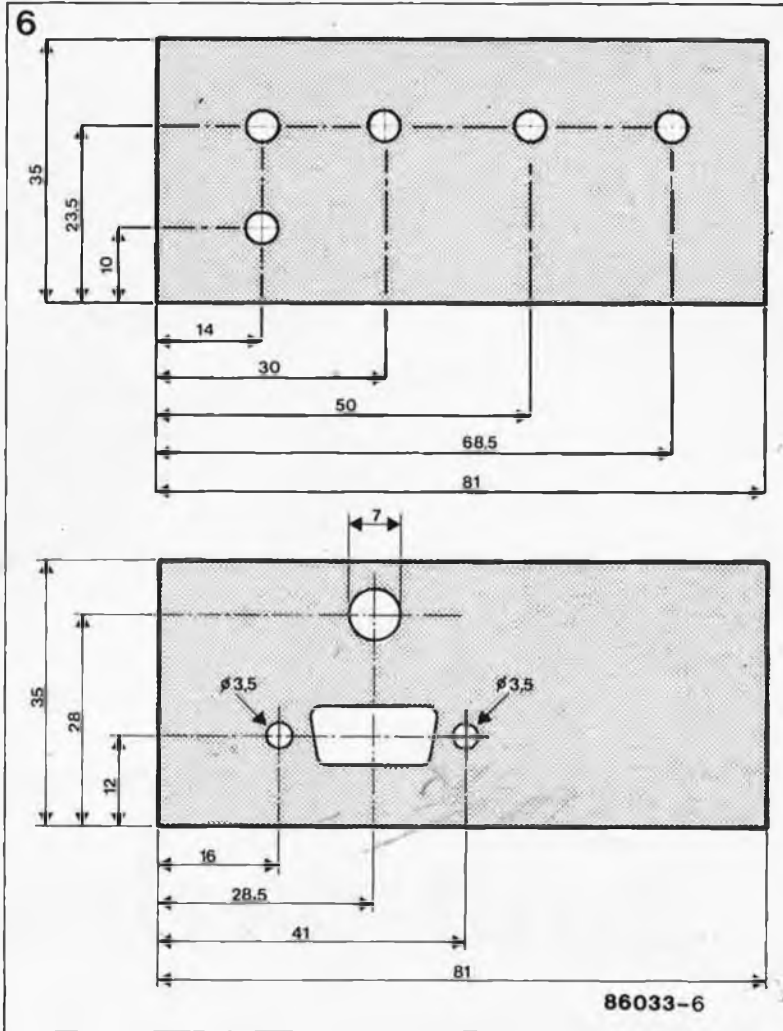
Gabarits de perçage des faces avant et arrière du modem.
